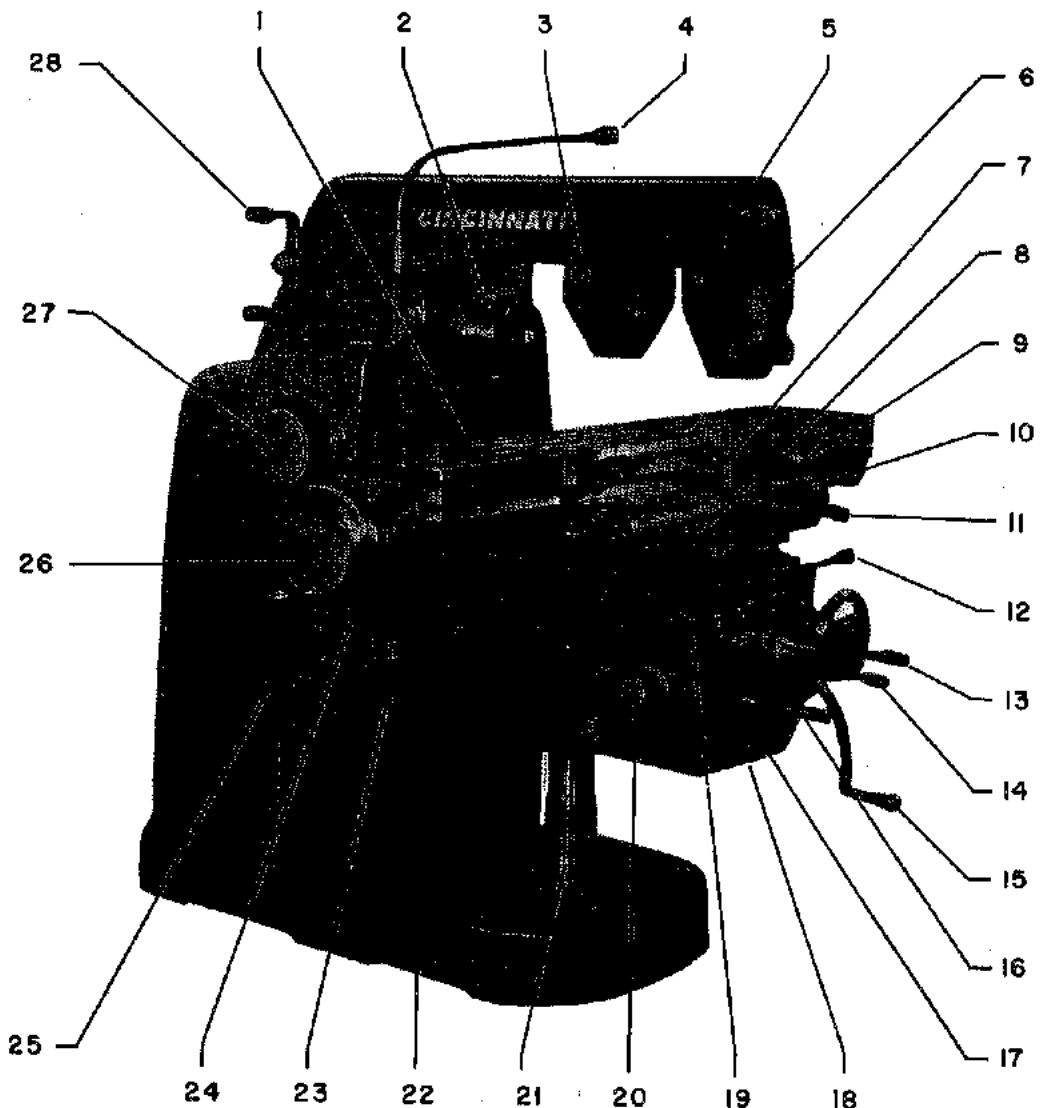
Nomenclatura de la fresadora corriente de columna y cartela, vista anterior (Cincinnati Milling Machine Co.)
